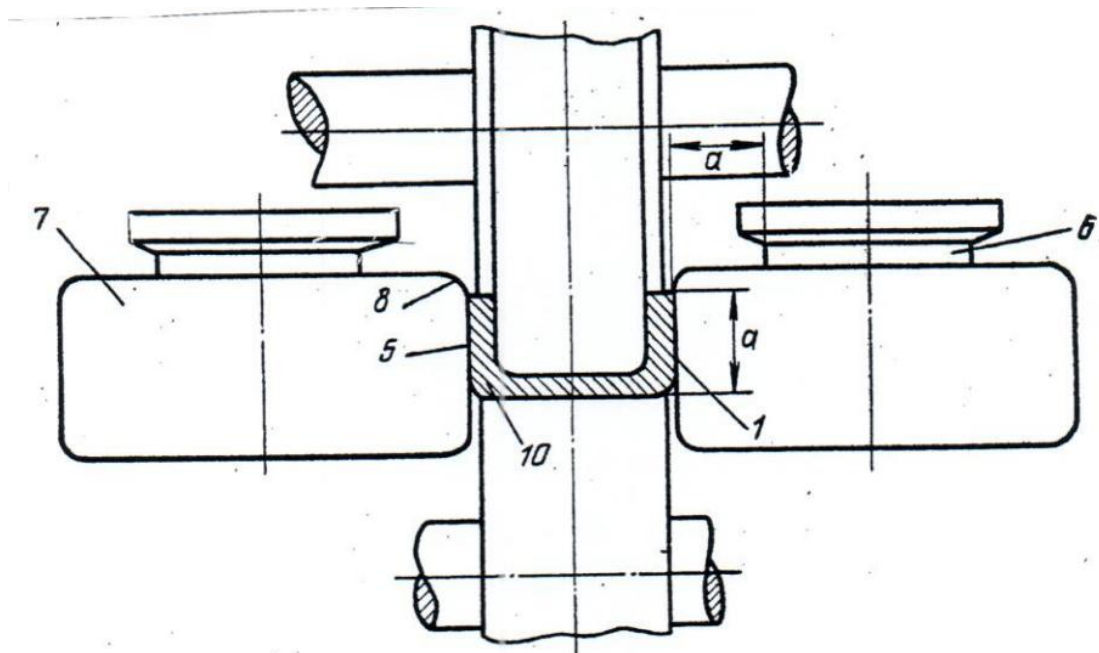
б. Состояние полосовой заготовки после формовки верхним и нижним горизонтальными валками
